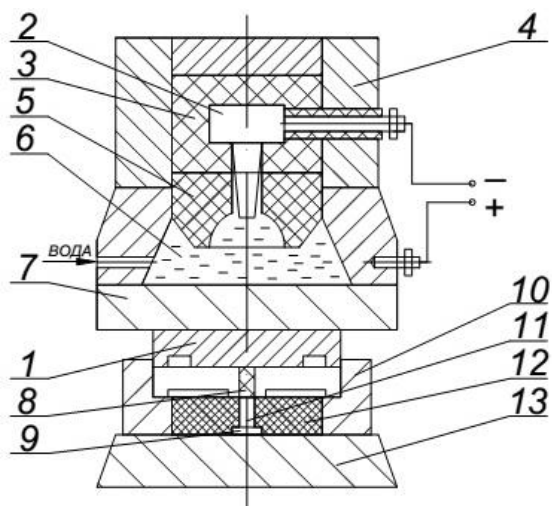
Схема взрывного прессования однокомпонентного абразивного инструмента: 1 – пуансон; 2 – катод; 3, 5 – изоляторы; 4 – корпус взрывной (разрядной) камеры; 6 – вода; 7 – плита; 8 – ударник; 9 – планка опорная; 10 – корпус пресс-формы; 11 – прессуемый абразивный порошок; 12 – матрица; 13 – стол пресса
